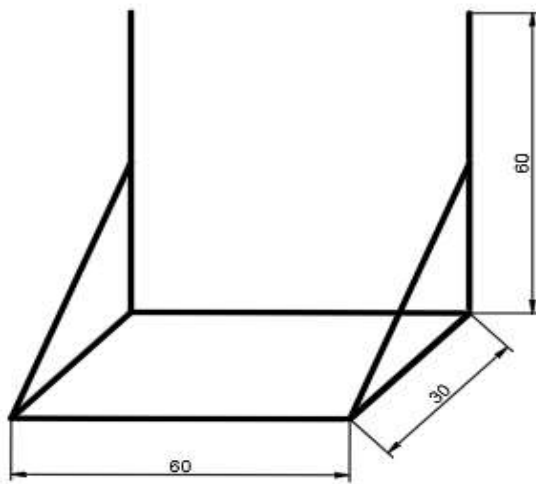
Dimensiones [cm] de estructura de soporte de caja del equipo de medición.
